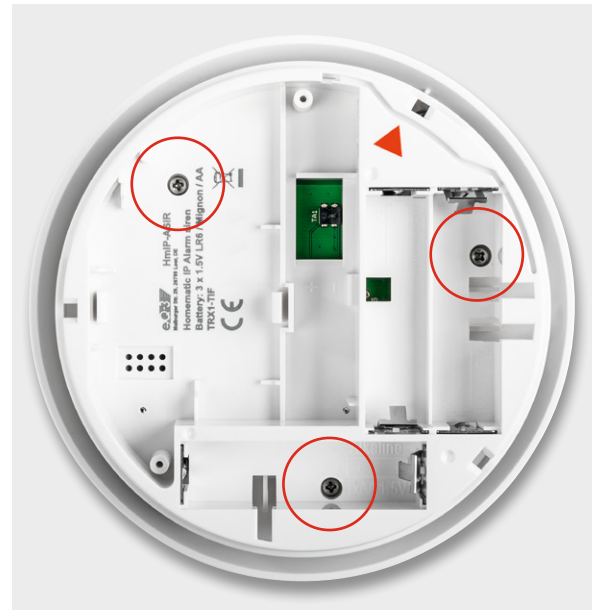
Die Gehäuseteile werden mit drei Schrauben verschraubt.
